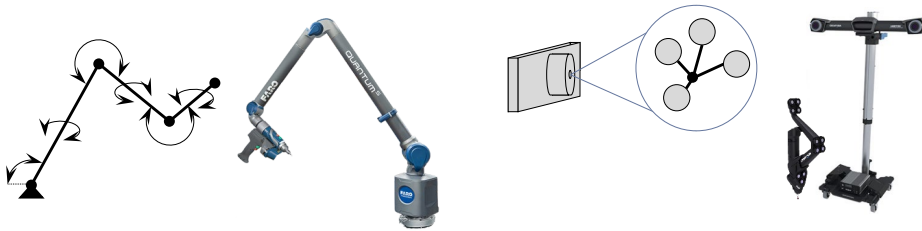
Prinzipien und Beispiele für Tracking bei Messwerkzeuge; mechanischer Gelenkarm [56] (links), optisch mit Kamera und Zielmarkern [57] (rechts).
